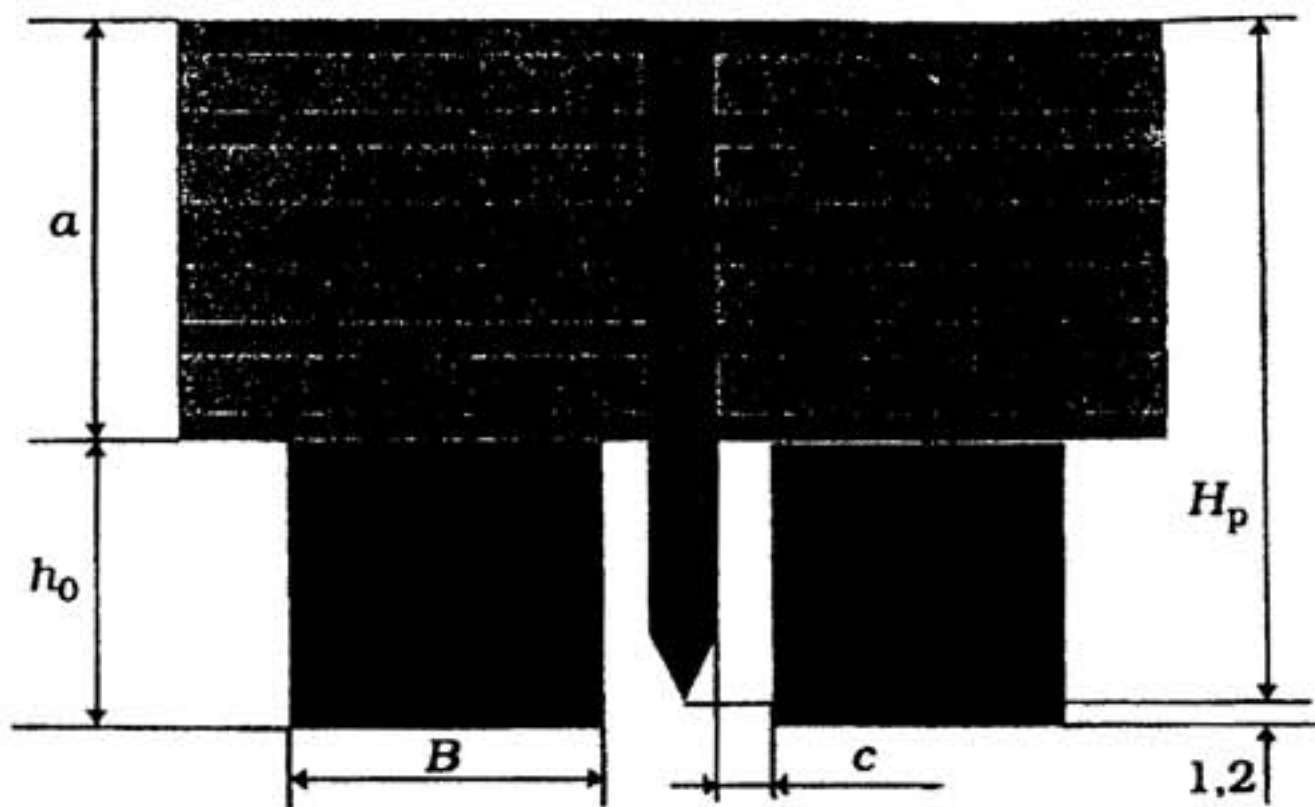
Схема расположения пружинящего элемента и режущего ножа
